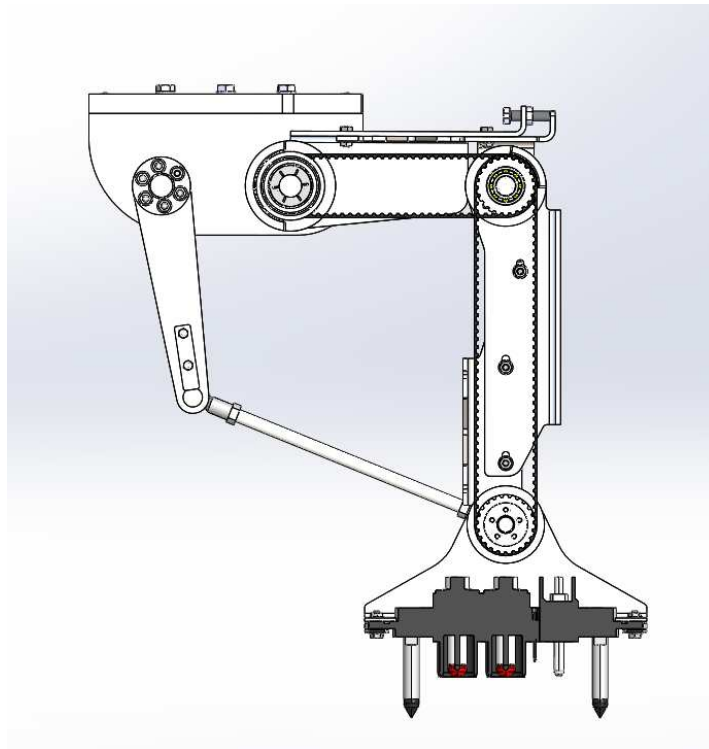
Secció en planta del disseny final, sistema de politges. (Font pròpia)
